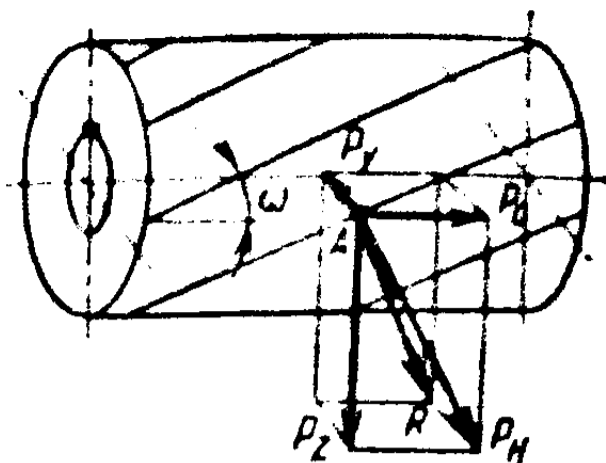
Составляющие силы резания при фрезеровании цилиндрической фрезой с винтовым зубом
